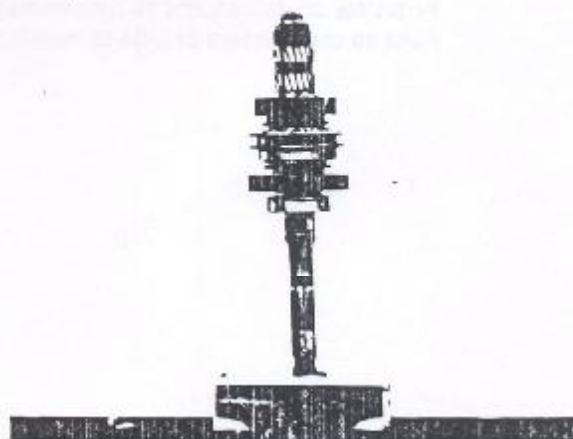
Conjunto sincronizador e engrenagem de 3ª removidos.
